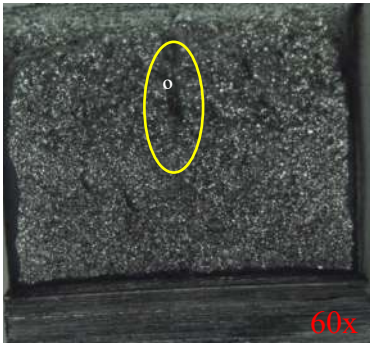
Vista macroscópica de la fractura, 22MnB5, -20°C, condición 1.
